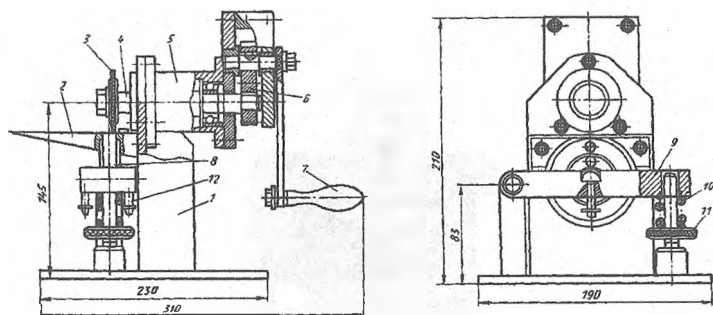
Приспособление для обесечки краев вкладных стелек
